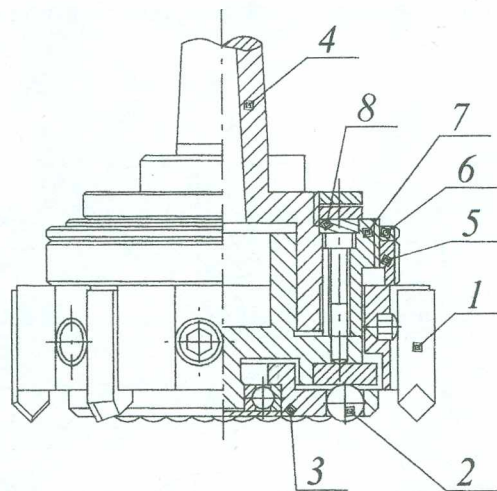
Фреза, комбінована з вигладжувальними кульками
